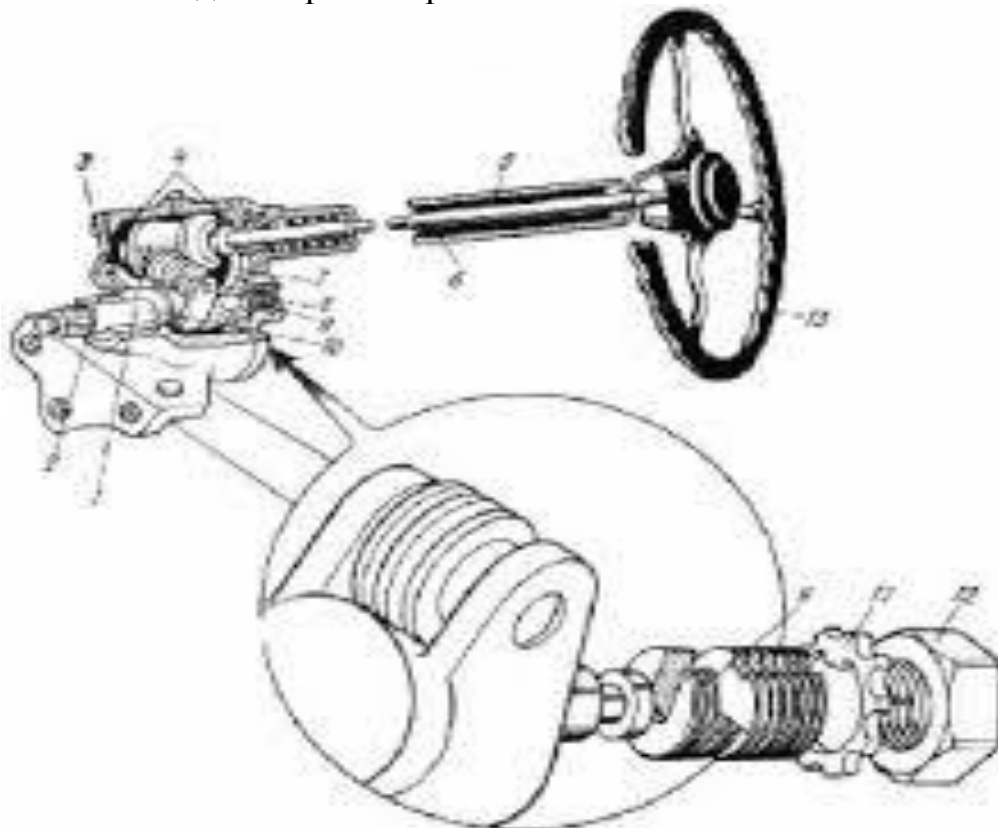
Регулировка рулевого механизма автомобиля ГАЗ(газель).
